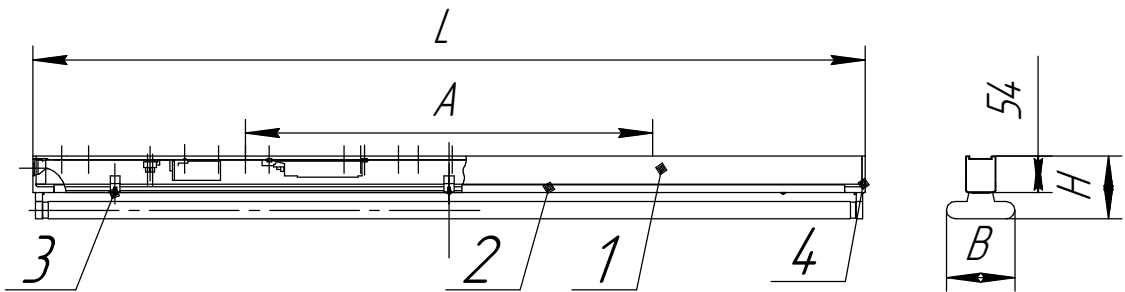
1. Корпус в сборе, 2. Крышка, 3. Винт, 4. Крышка.
